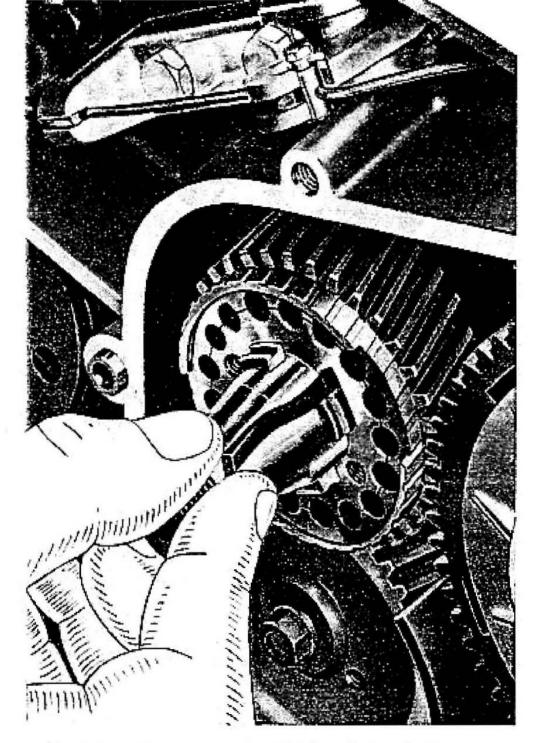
Come viene montata la molla a balestra per pignone elastico motore.
